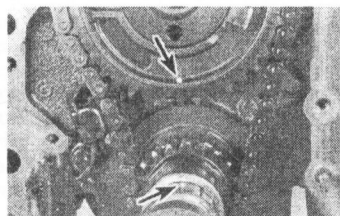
Метки на звездочках коленвала и распредвала (показаны стрелками) должны встать напротив друг друга (метка на звездочке распредвала представляет собой выемку, а метка на звездочке коленвала – небольшой выступ).
